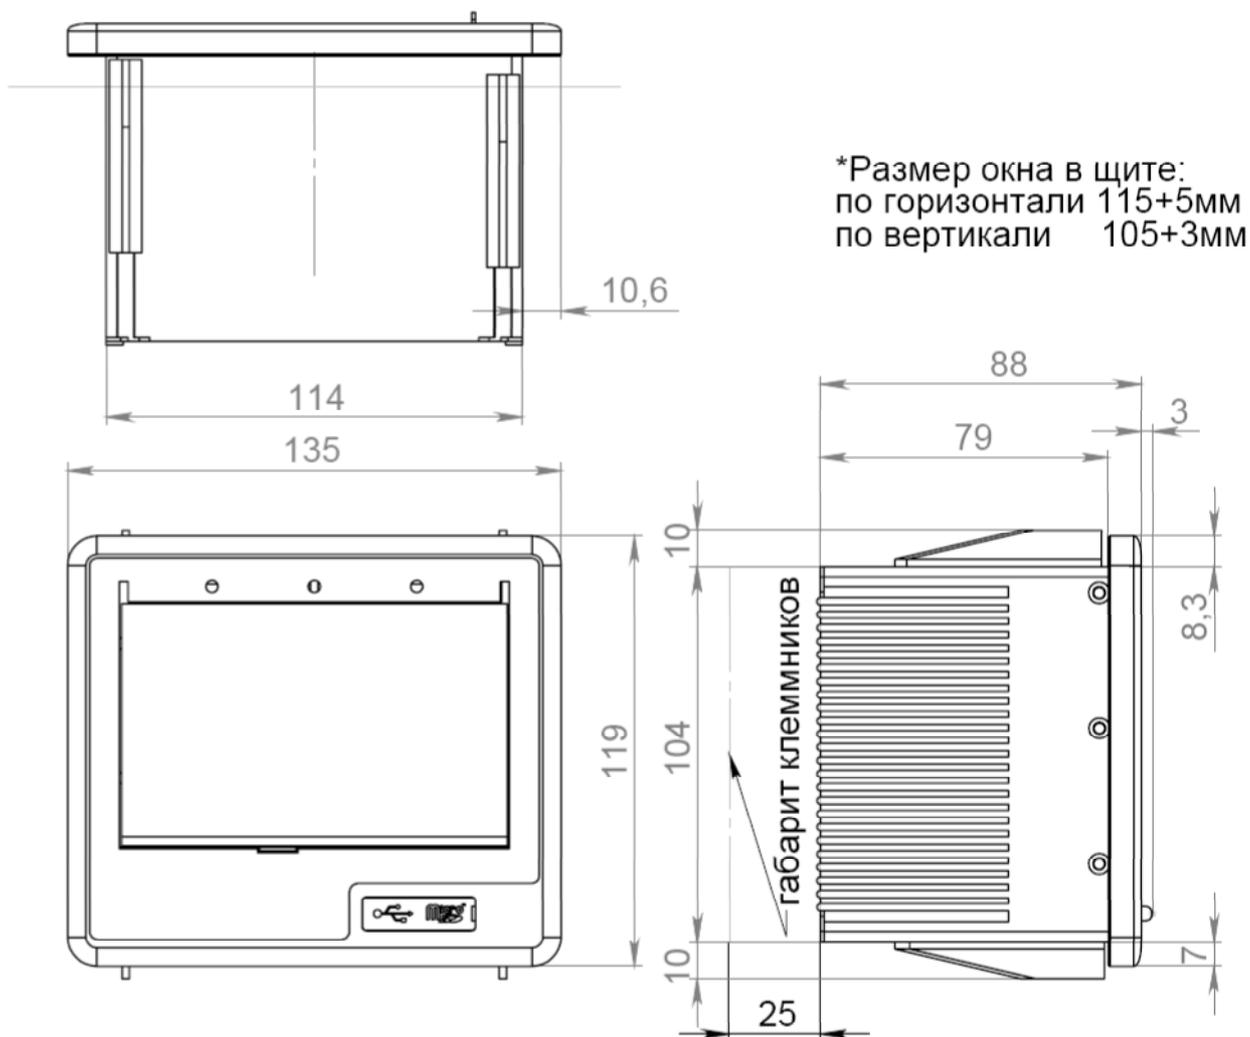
Габаритные размеры АГАВА ПК-40.04
